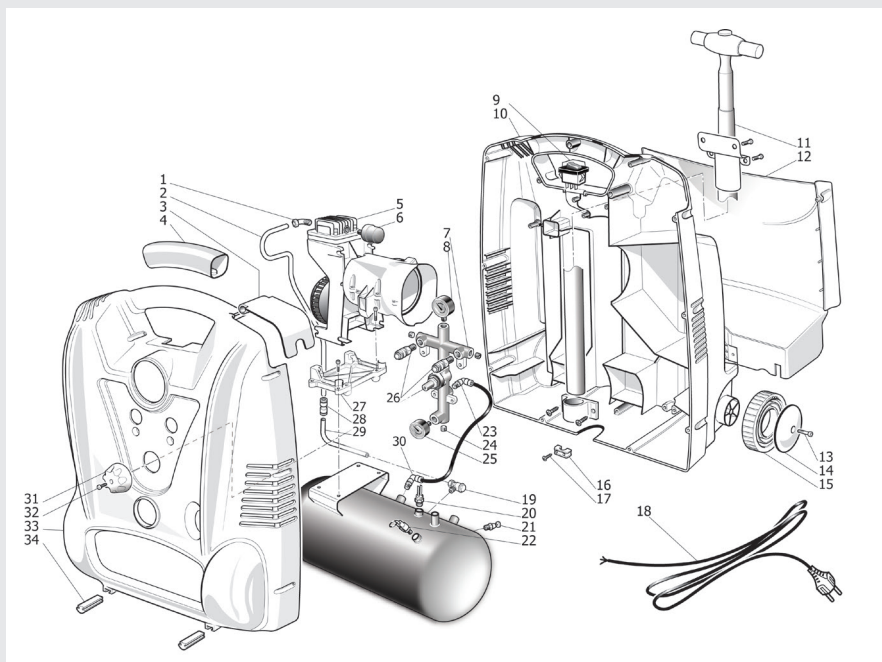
Explosionszeichnung (Abb. ähnlich)
